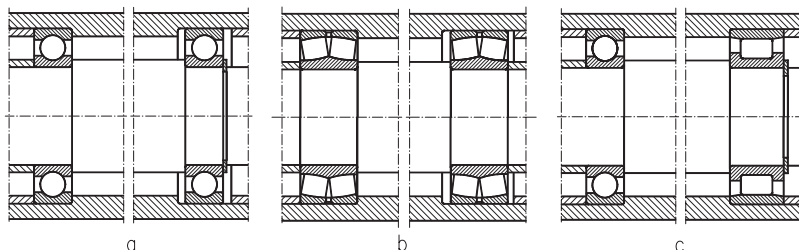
Подшипниковые узлы с фиксированными и свободными подшипниками
